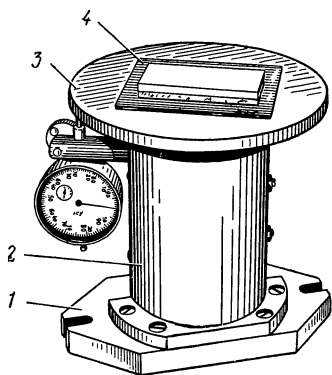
Специальный пружинный стол для рабочей подачи заготовок
